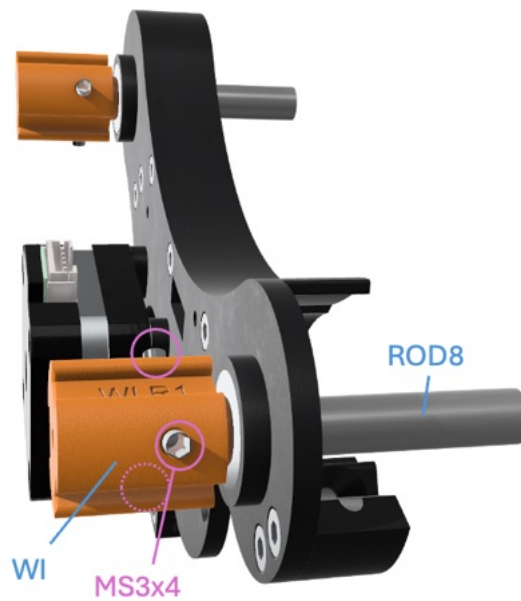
Rewinder-Chassis Montageschritt 11.
